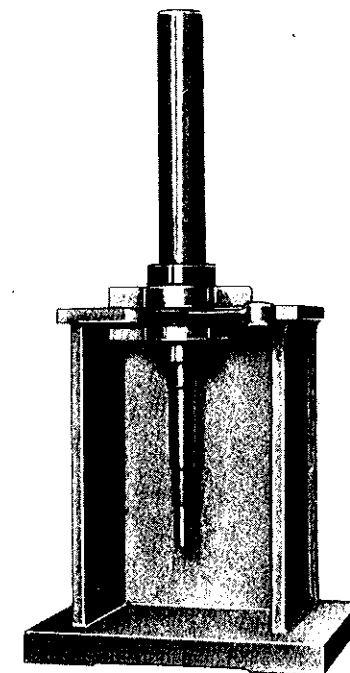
Ringrillennager erhitzen und auf Kurbelwelle aufziehen
